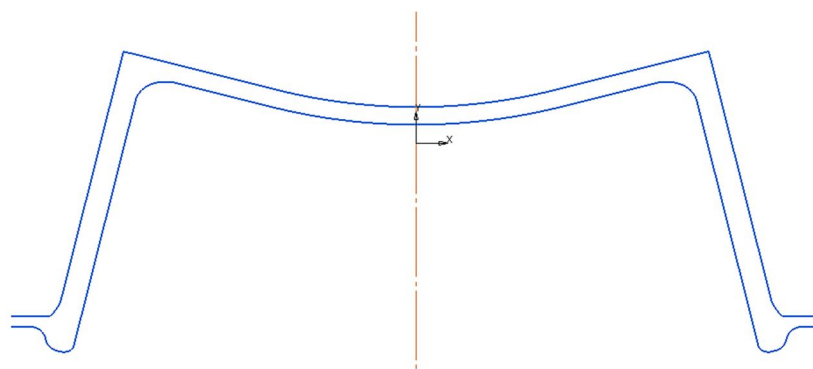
Чертеж калибра клети № 16Г с выравниванием горизонтального элемента профиля
